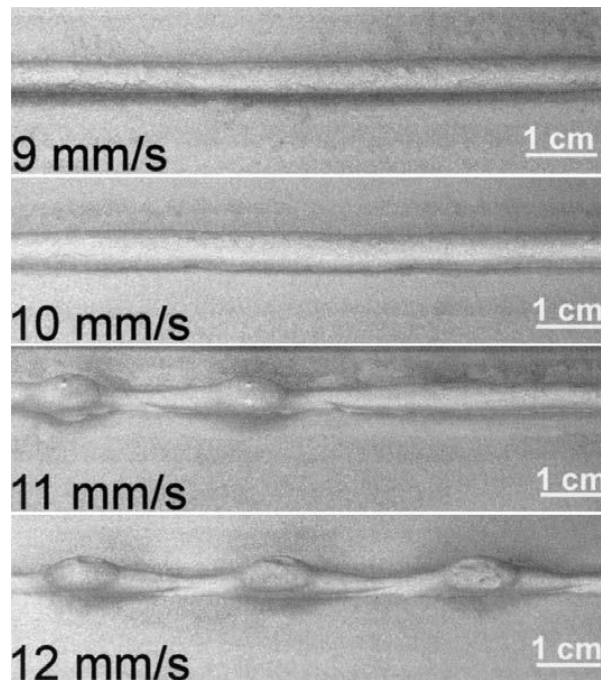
Pravidelné zvlnění svaru – boulování [13]
